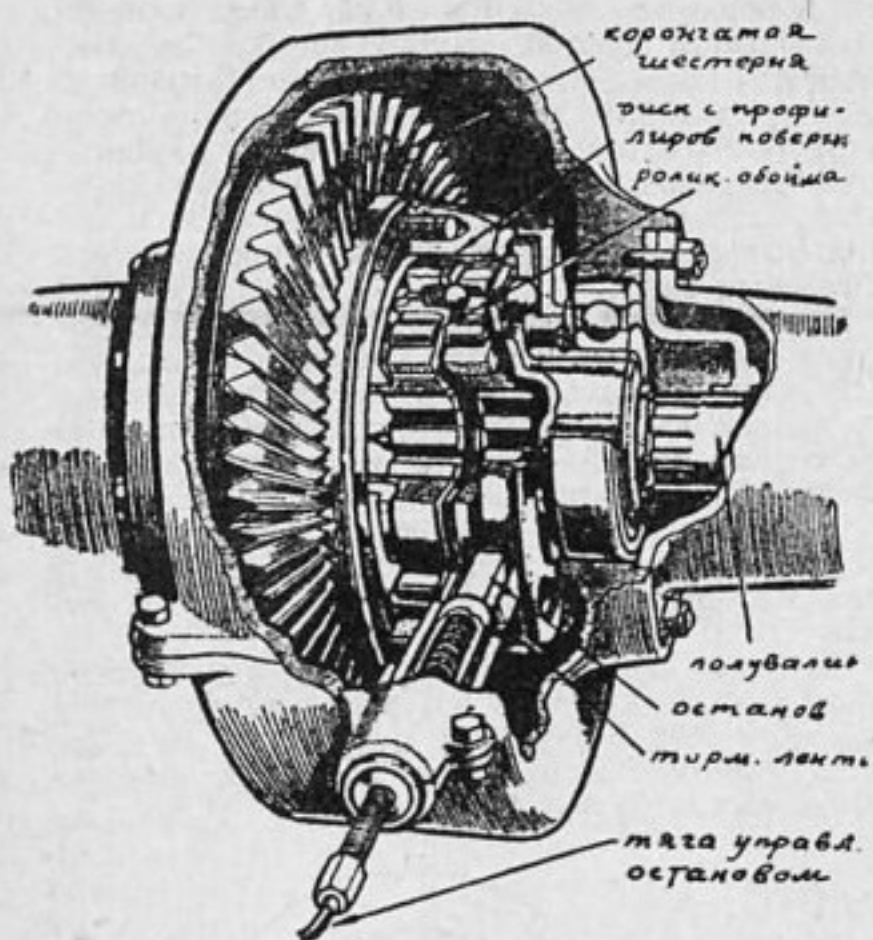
Собранный механизм свободного колеса „Ляво“. Видны замыкающая тяга и пружинный останков
